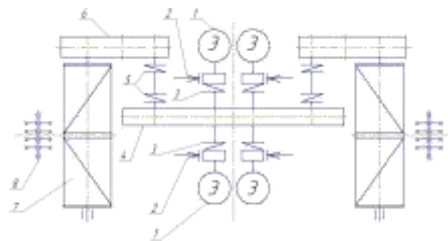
Конструкция с тройным планетарным шестеренчатым редуктором (компания Урал-Шталь) (схема №5)
